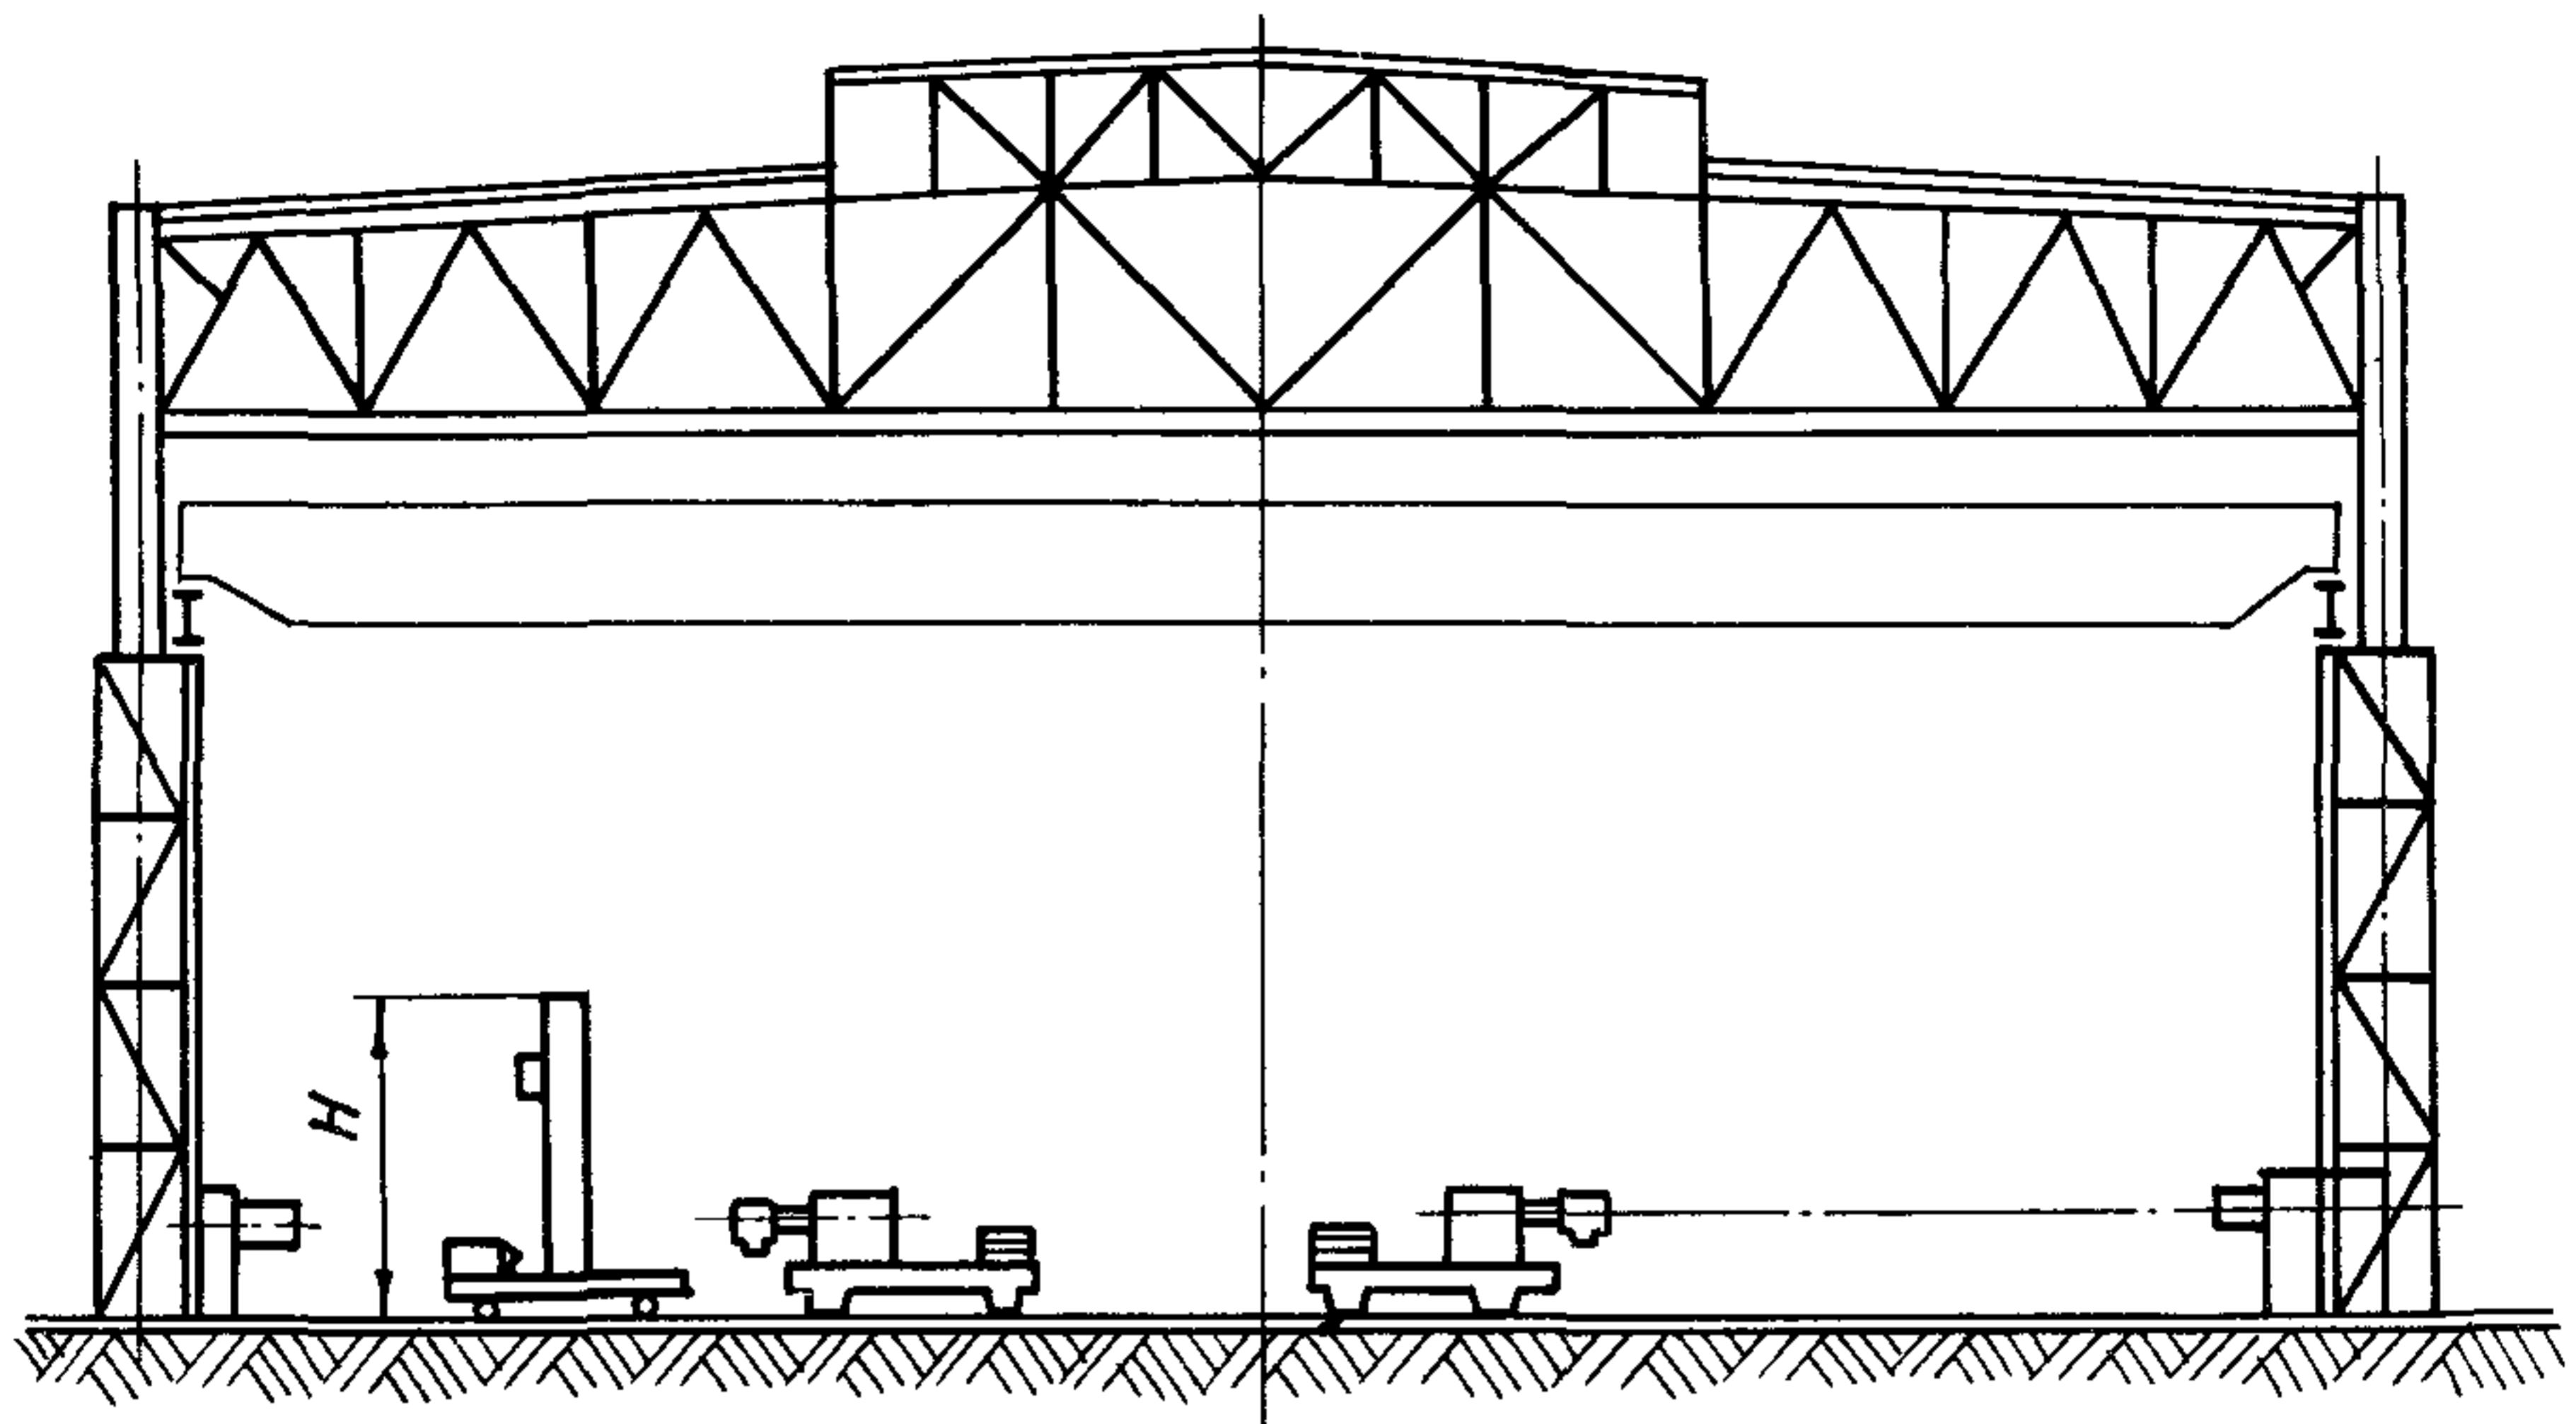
Размещение участка автоматической сварки с глгольной тележкой:
